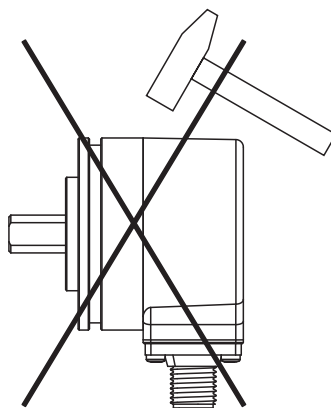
Montageansicht – nicht mit dem Hammer ausrichten
